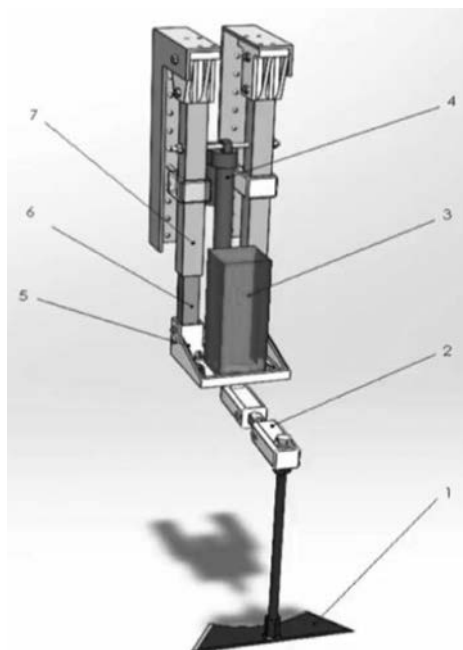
Устройства для прополки в рядах пропашных культур: 1 – прополочный нож; 2 – поворотная стойка; 3 – шаговый двигатель; 4 – линейный актуатор; 5 – консоль привода; 6 – внутренняя направляющая; 7 – наружная направляющая
